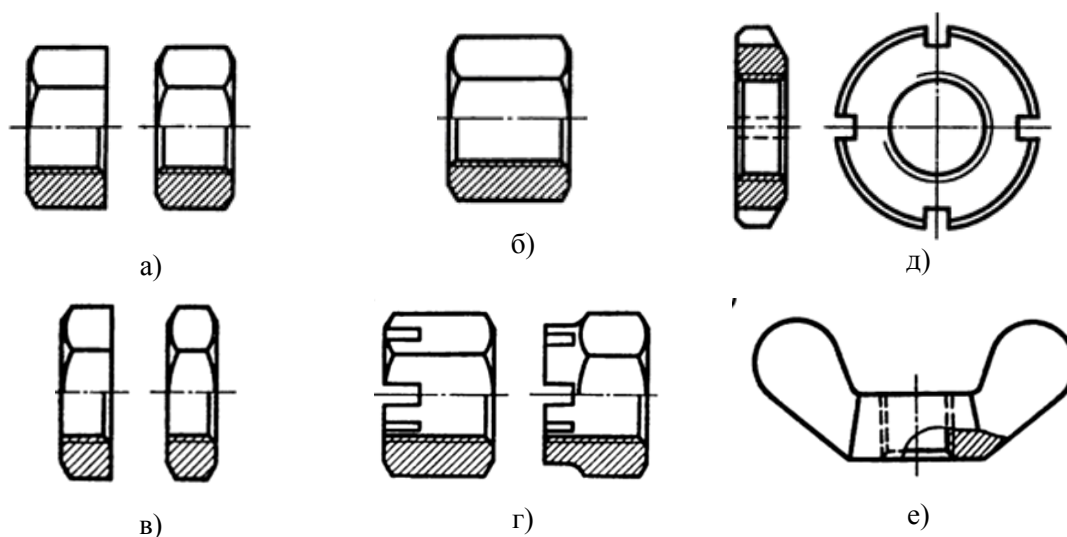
Гайки: шестигранные: а – нормальные (с одной и двумя фасками); б – высокие; в – низкие; г – прорезные и корончатые; д – круглые; е – гайки-барашки
